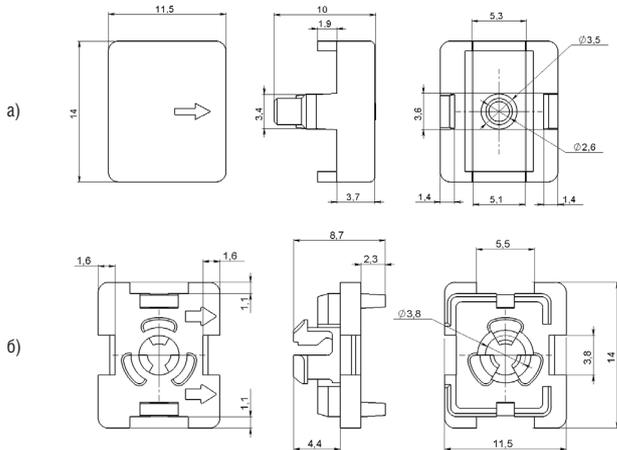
Габаритные размеры заглушки ВА47-29
